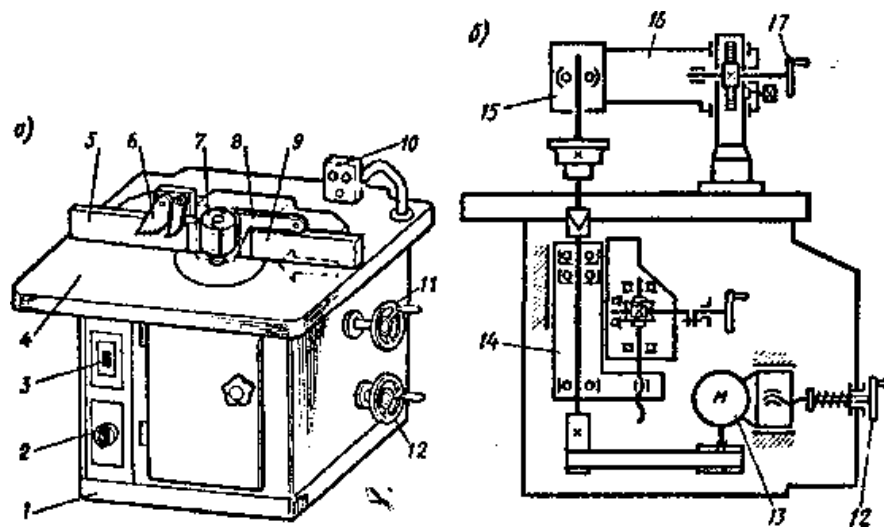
Одношпиндельний фрезерний верстат з ручною подачею ФС–1: а – загальний вигляд; б – кінематична схема; 1 – станина; 2 – перемикач частоти обертання шпинделя; 3 – вимикач; 4 – стіл; 5, 9 – направляючі лінійки; 6 – зубчатий сектор; 7 – ріжучий інструмент (фреза); 8 – огорожа; 10 – пульт управління; 11 – маховичок налаштування шпинделя по висоті; 12 – маховичок натягнення ремня; 13 – електродвигун; 14 – шпиндель; 15 – додаткова опора шпинделя; 16 – кронштейн; 17 – маховичок підйому кронштейна.
